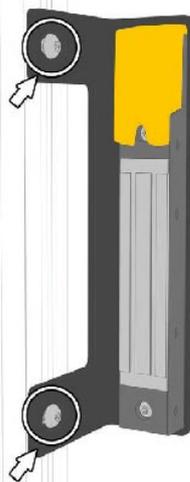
Montageplatte mit Prozesszuhaltung am Profil anbringen und und Schrauben M8 x 12 mm Torx festziehen.
